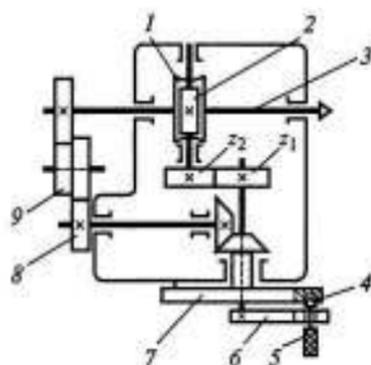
Схема наладки универсальной лимбовой головки на простое деление; 1 — червячное колесо; 2 — червяк; 3 — шпindel; 4 — стопор; 5 — рукоятка; 6 — сектор; 7 — делительный диск; 8, 9 — зубчатые колеса; z_1, z_2 — шестерни
